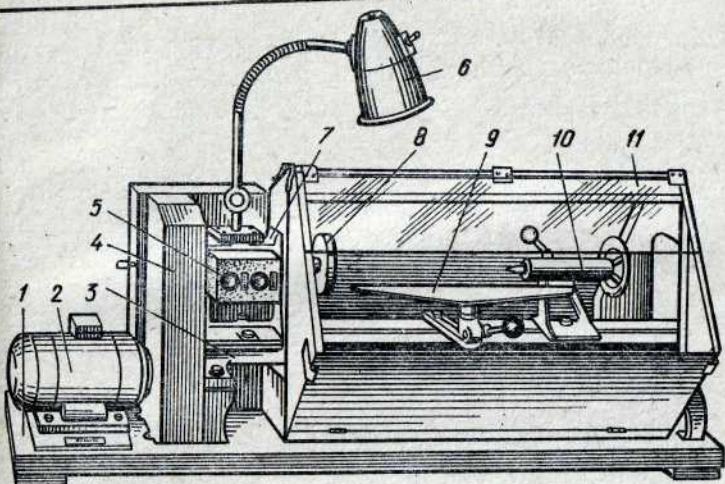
Токарный станок по обработке древесины: 1 — основание; 2 — электродвигатель; 3 — станина; 4 — ограждение ременной передачи; 5 — магнитный пускатель; 6 — светильник; 7 — передняя бабка; 8 — шпиндель; 9 — подручник; 10 — задняя бабка; 11 — защитный экран.
